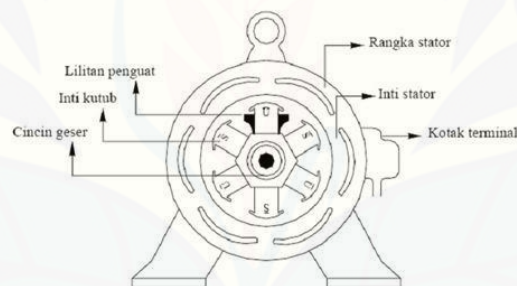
Konstruksi umum motor induksi 1 fasa (Sumber: Sinaga, 2011)
